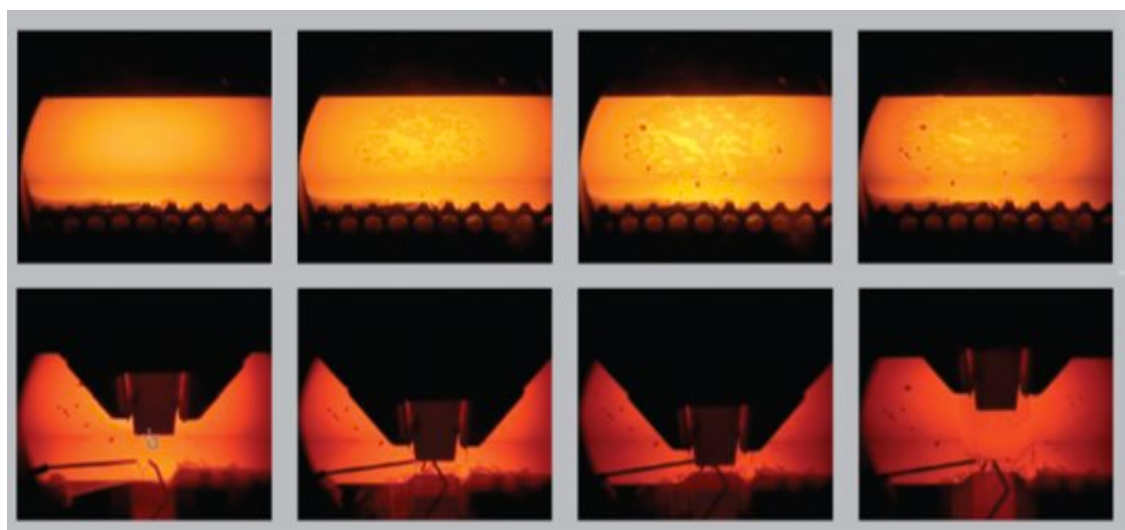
Образец, подвергаемый плавлению, затвердеванию и горячей деформации
